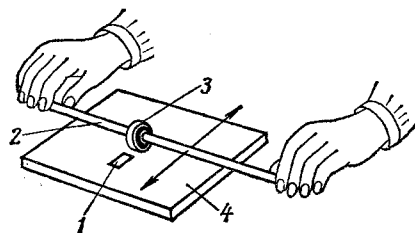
Изготовление прокладки рабочего зазора универсальной головки: 1 — заготовка, Бр. В2; 2 — стержень, Ст. 45; 3 — подшипник шариковый № 23; 4 — стекло.
